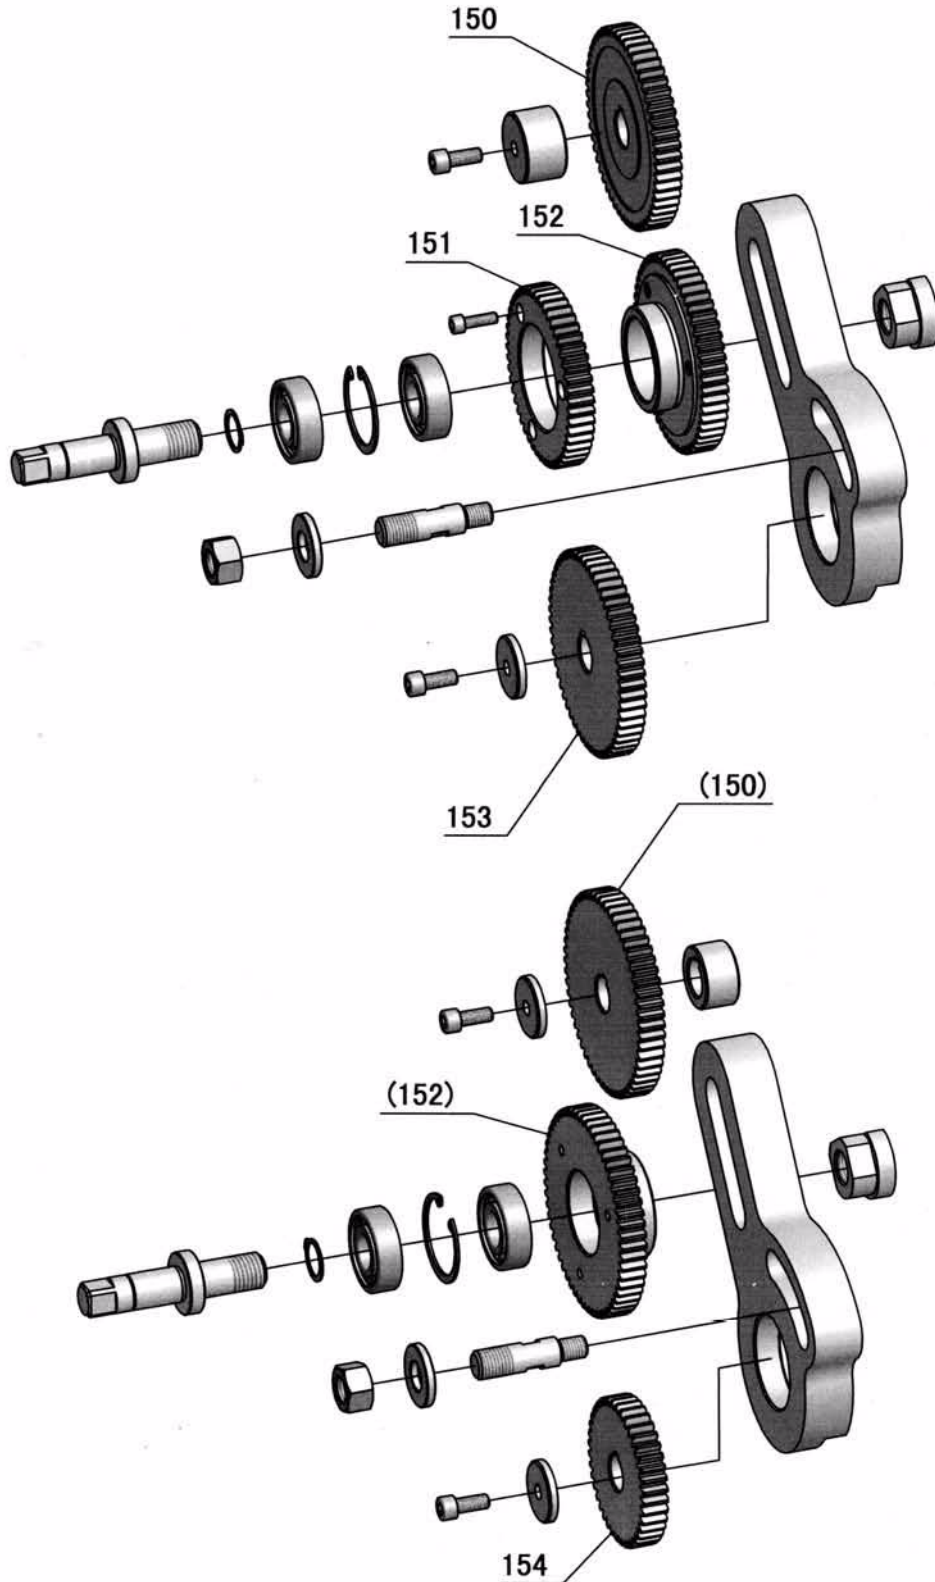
Wechselradgetriebe (Inch) - Change wheel gear (Inch)
